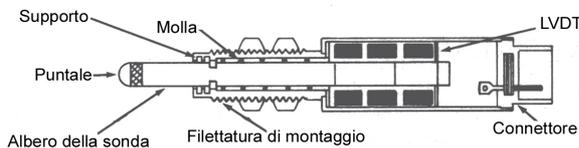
Sezione di una tipica testa di misura ad LVDT
